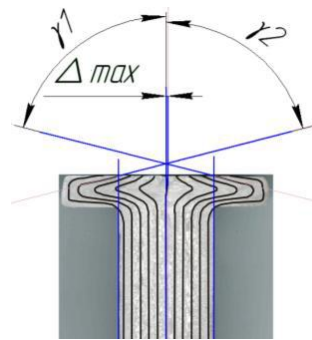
Волокниста структура заготовки типу стрижня з фланцем
